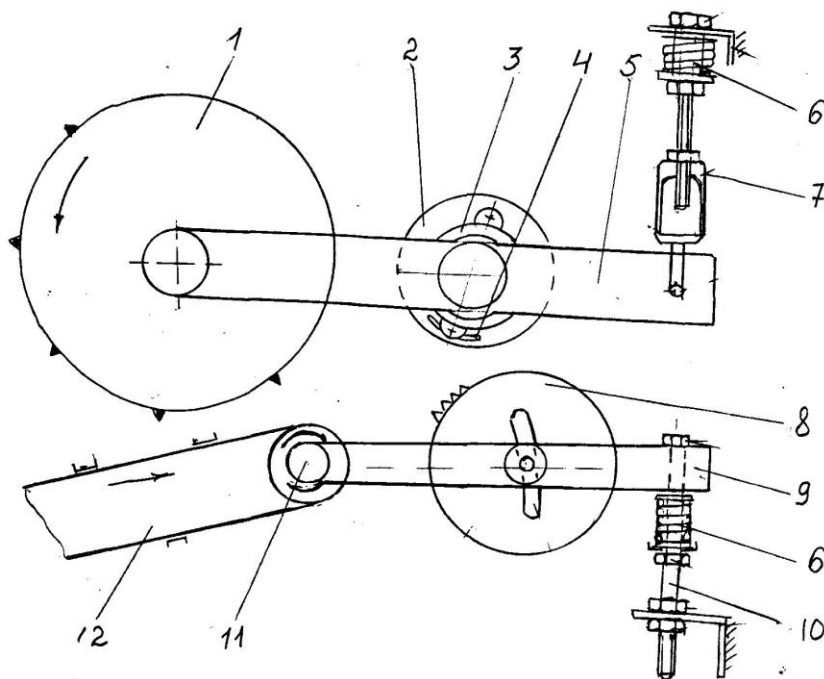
Механизм регулировки зазоров: 1 – питающий барабан; 2 – гладкий валец; 3 – опора кронштейна; 4 – радиальный паз стенки питающего устройства; 5 – двухплечий кронштейн; 6 – натяжные пружины; 7 – тяга; 8 – нижний битерный барабан; 9 – кронштейн; 10 – регулировочная тяга нижнего барабана; 11 – опора вала скребкового транспортера; 12 – транспортер жатки
